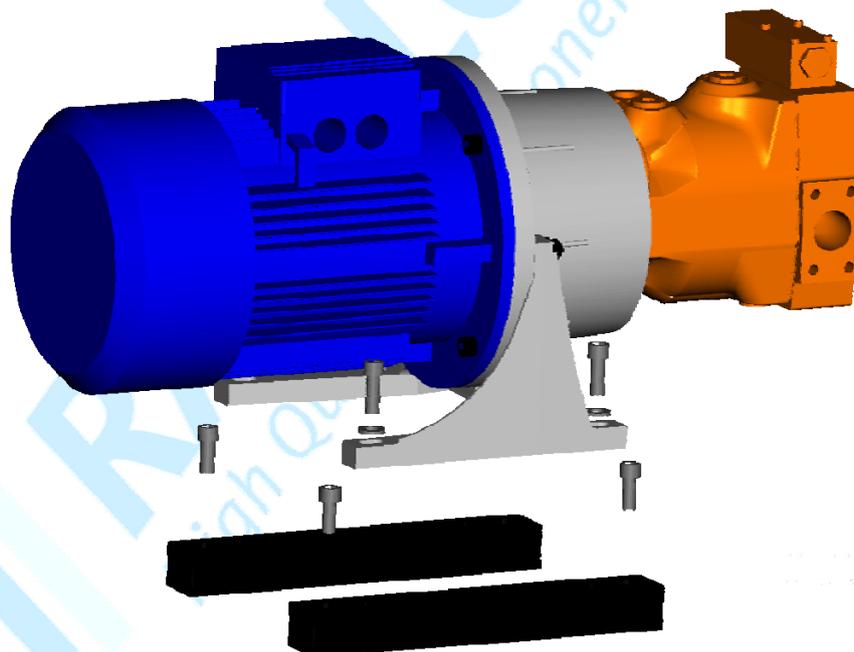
Explosionszeichnung: Dämpfungsschienen PTFS - Elektromotor
